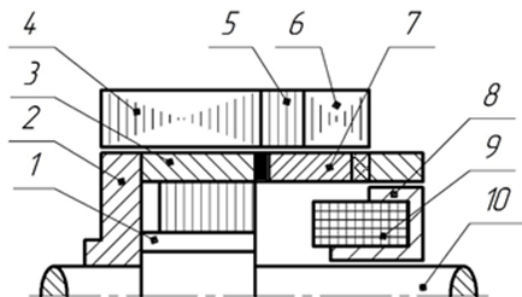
Эскиз продольного сечения БСГКВ с «активным» шунтом при однопакетном исполнении: 1 – немагнитная втулка; 2 – униполярная пластина; 3 – полюсный наконечник; 4 – статор опорного генератора; 5 – немагнитная прокладка; 6 – статор регулировочного звена; 7 – полюсная система регулировочного звена; 8 – скоба; 9 – обмотка возбуждения; 10 – вал из магнитомягкого материала
